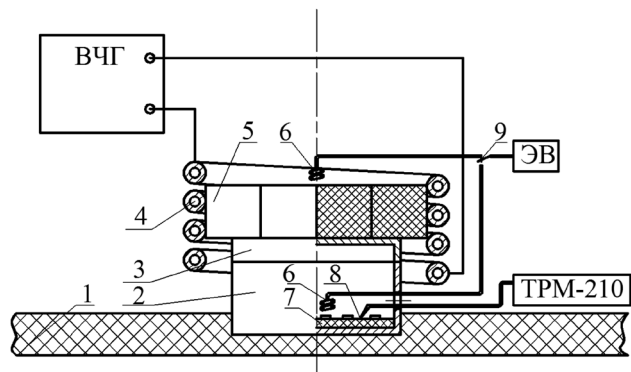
Схема ВЧ-нагрева для герметизации корпусов микроблоков:
